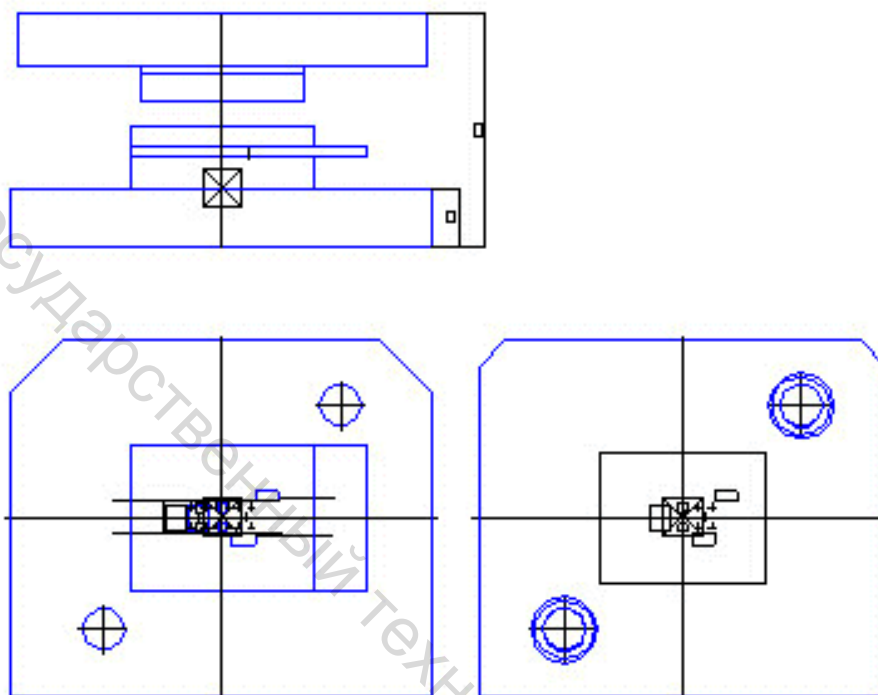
Сборочный чертеж штампа с изображением блока
